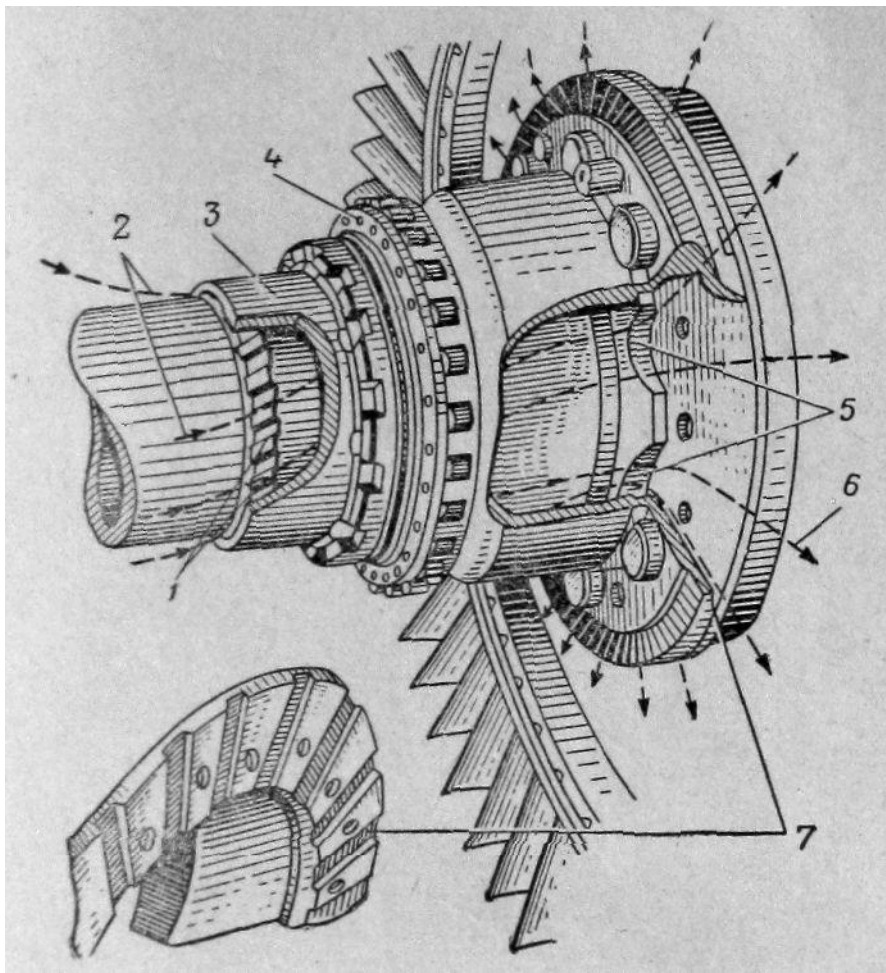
Схема охлаждения заднего роликоподшипника: 1 — спиральные канавки на валу колеса турбины; 2 — вход воздуха под втулку; 3 — втулка вала колеса турбины; 4 — задний роликовый подшипник; 5 — канавки для прохода воздуха на заднем посадочном пояске вала; 6 — выход охлаждающего воздуха; 7 — радиальные канавки втулки вала колеса турбины
